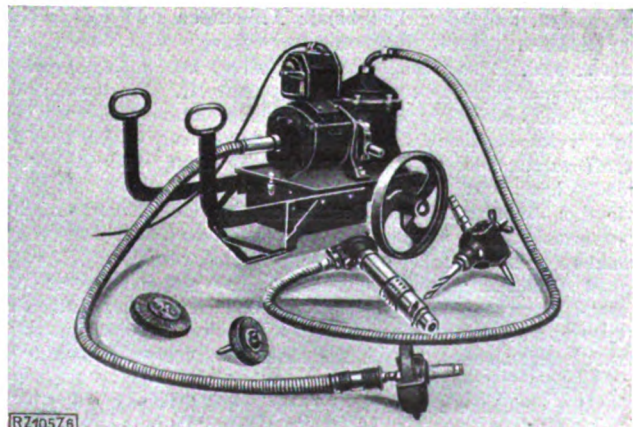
Fahrbarer Elektrokompessor für Druckluftwerkzeuge; C. & E. Fein, Stuttgart.
